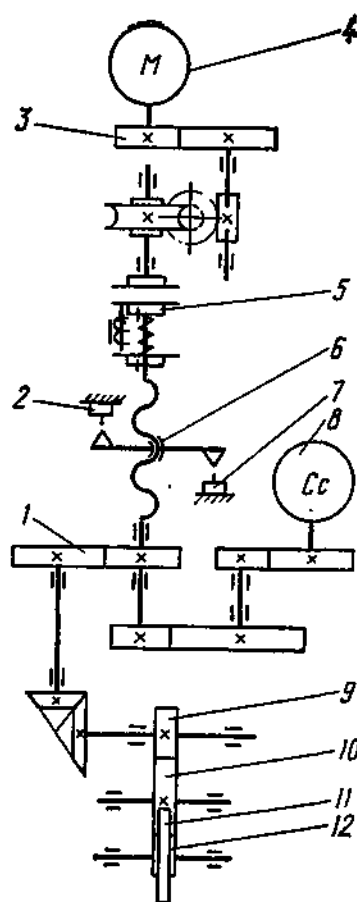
Исполнительный механизм КС—А3 реактора МИР:
